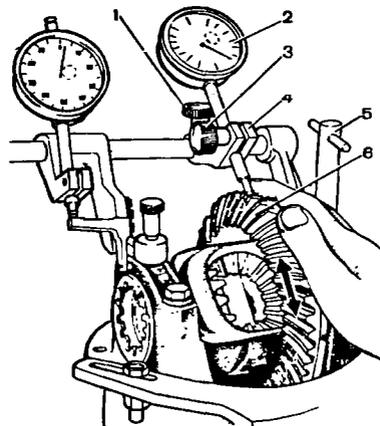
Проверка бокового зазора в зацеплении шестерен главной передачи приспособлением А.95688/Р: 1 - винт затягивания кронштейна; 2 - индикатор для проверки бокового зазора в зацеплении ведущей и ведомой шестерни; 3 - винт крепления стержня индикатора; 4 - кронштейн индикатора; 5 - винт крепления; 6 - ведомая шестерня
